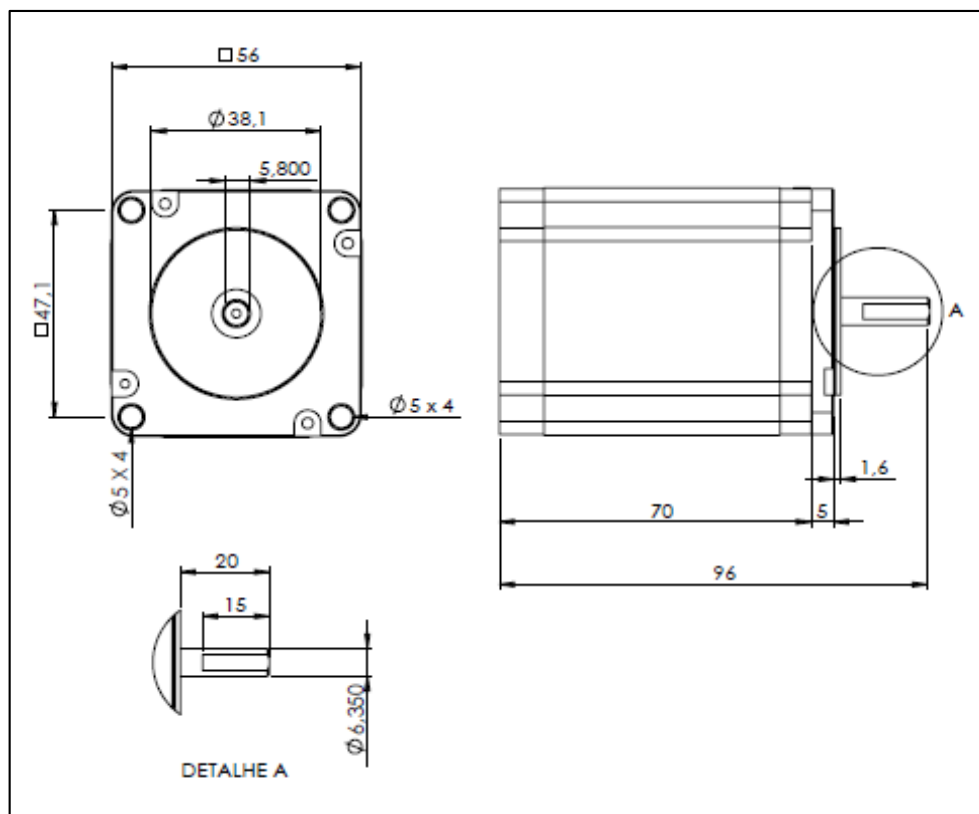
Desenho técnico 2D do motor de passo AK23/15F6FN1.8 – AKIYAMA
